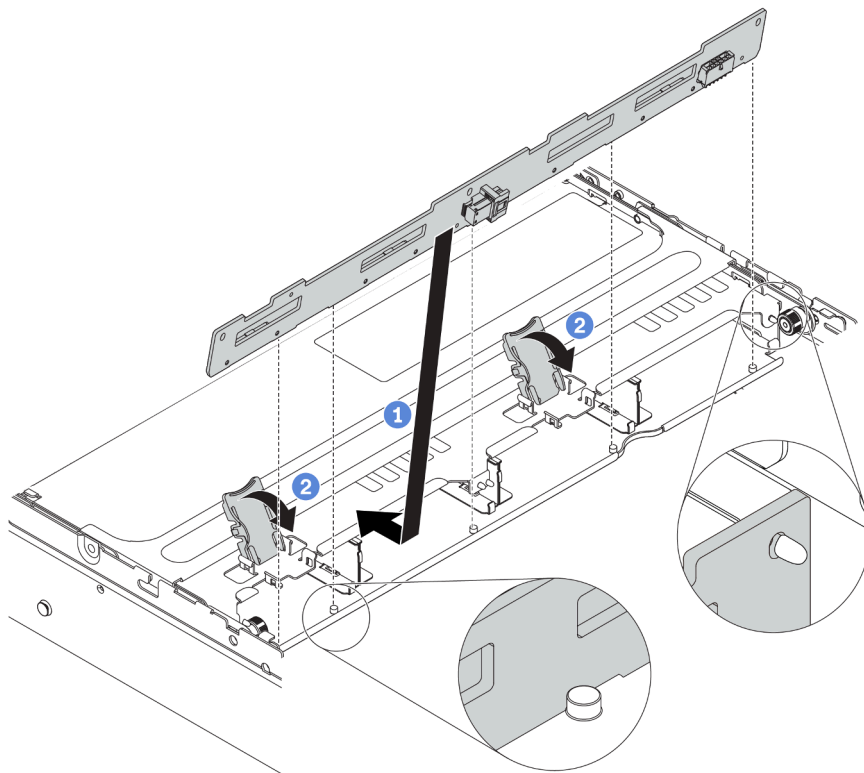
Installation du fond de panier d'unité central 3,5 pouces
